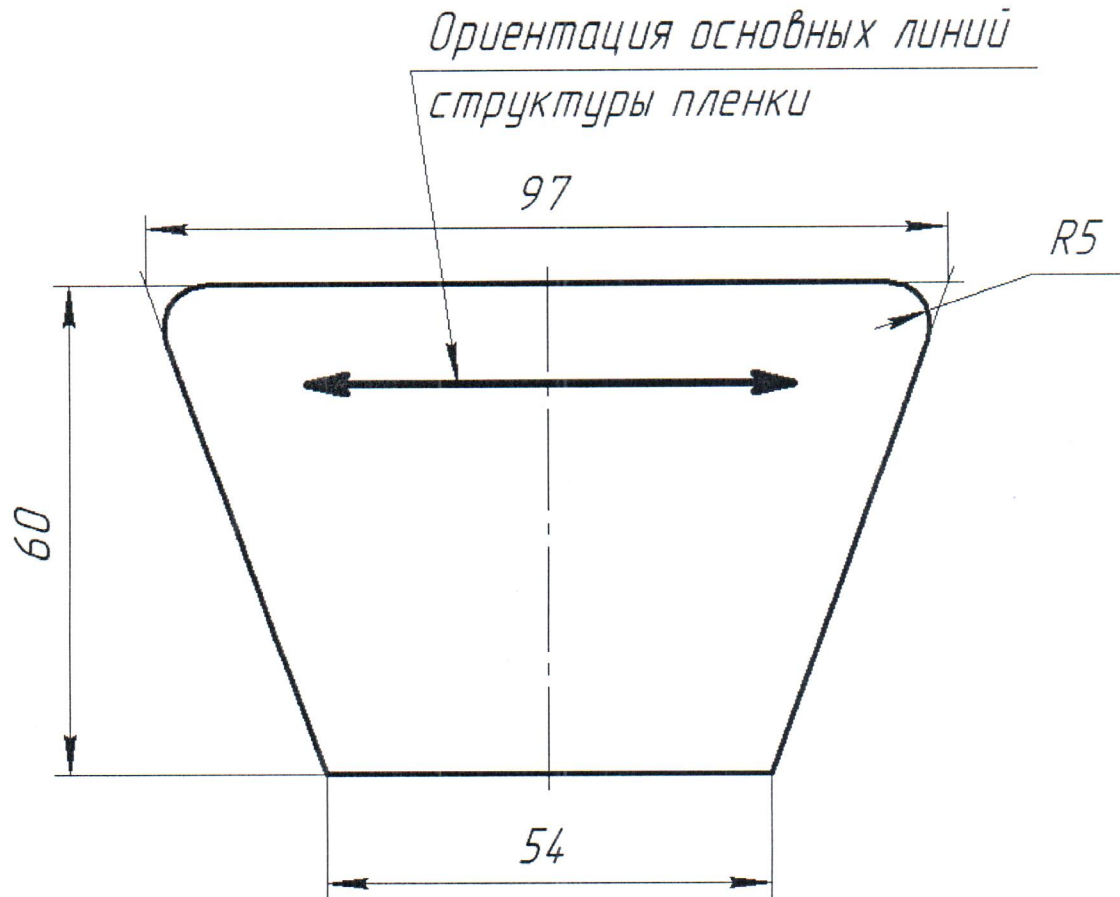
Корпус световозвращателя КД5-КБII-R1
